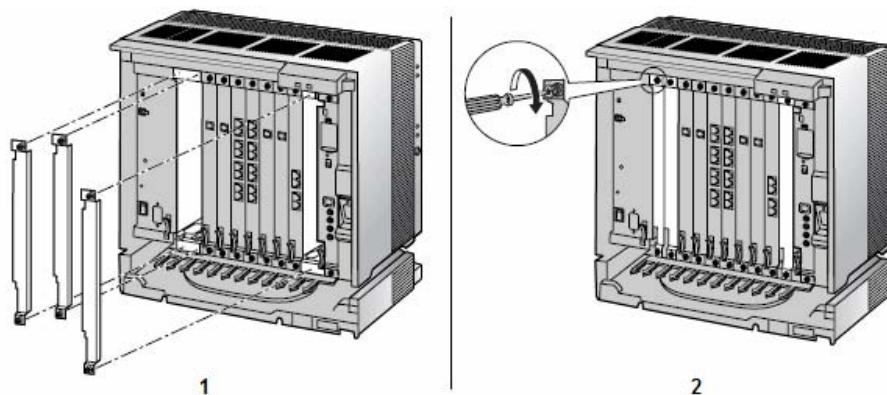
Instalación de cubiertas de ranuras en blanco.
